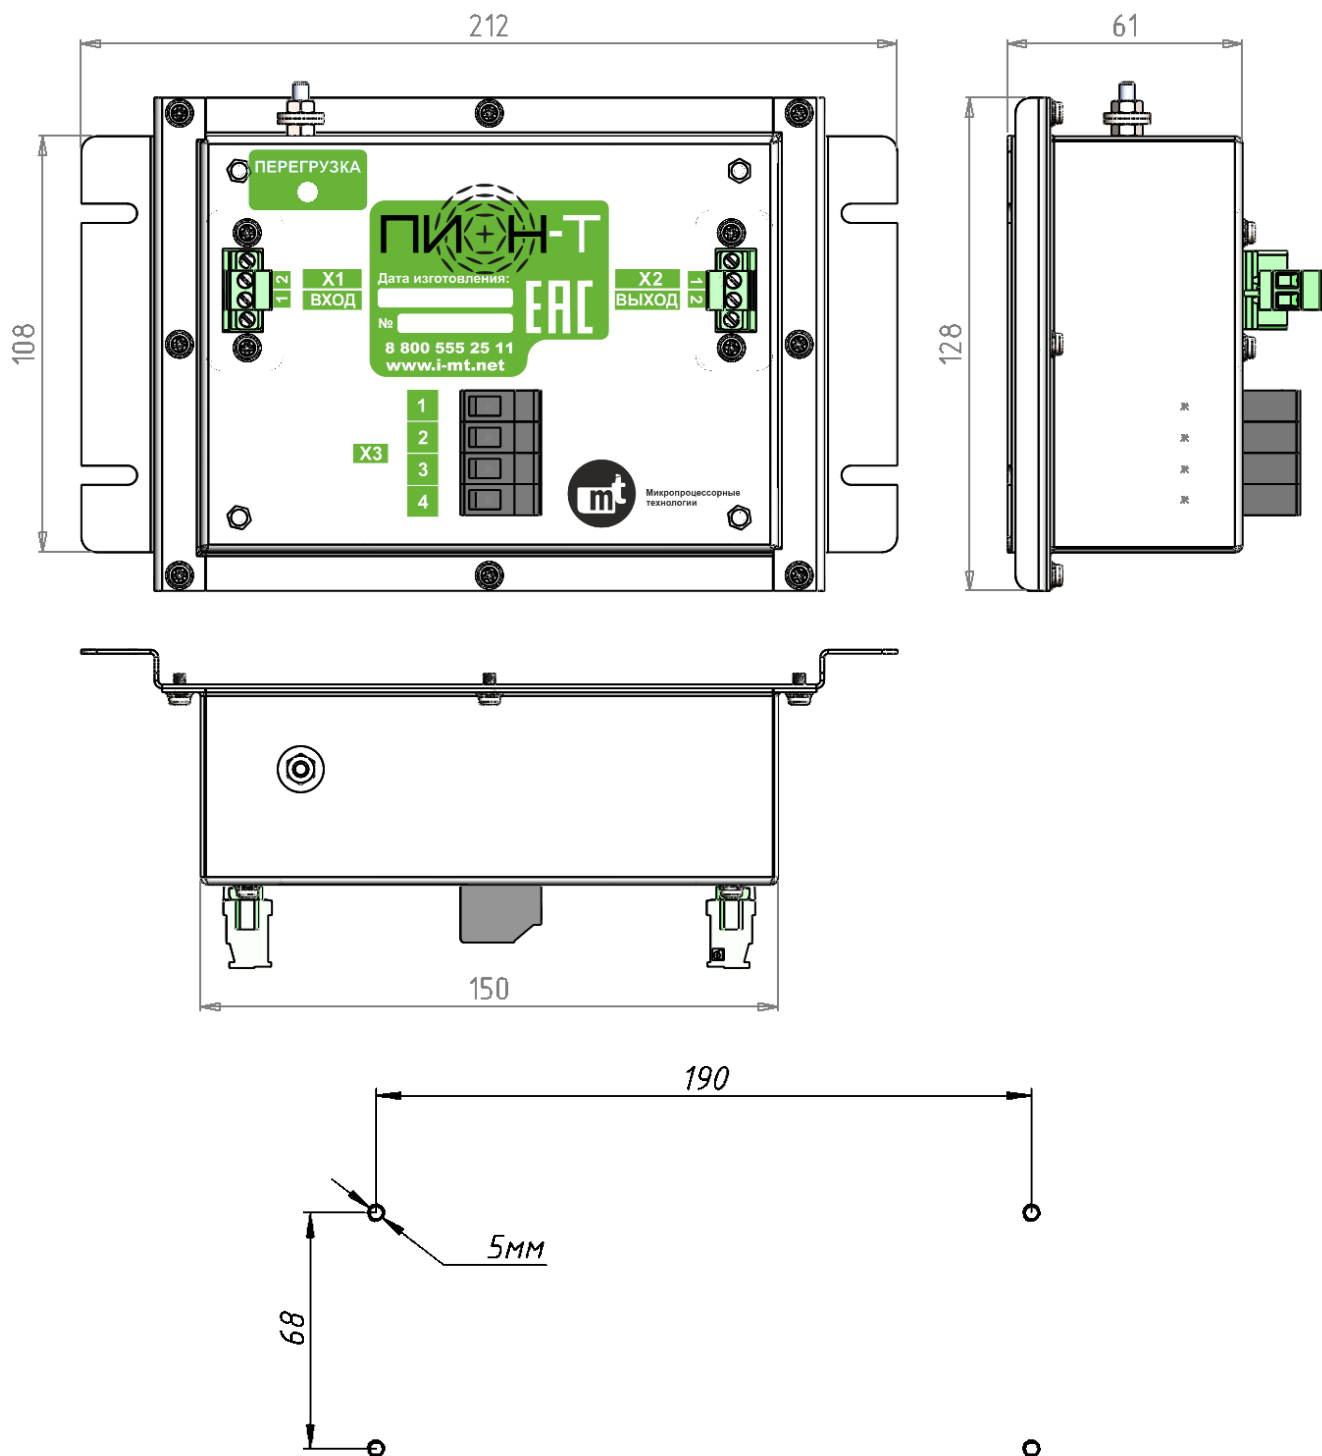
Габаритные размеры и расположение отверстий для крепления блока питания Пион-Т
